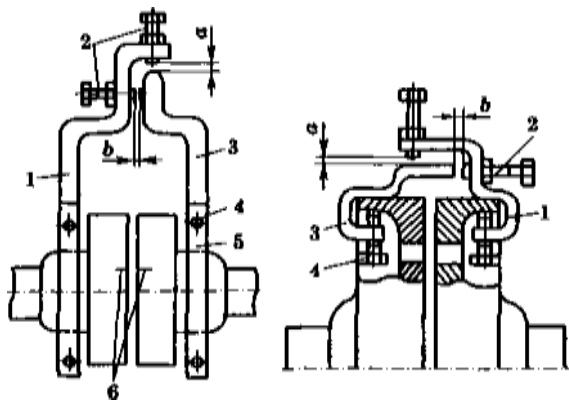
Центровка валов: *a* — центровочные скобы для центровки по втулкам полумуфт;
